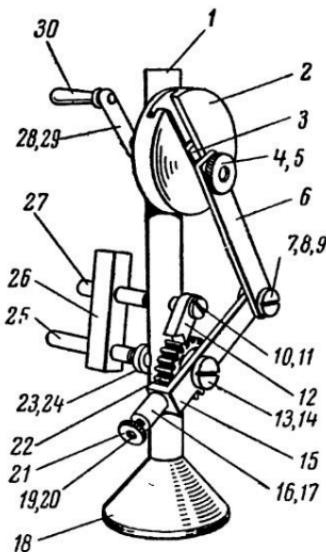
Модель механизма подачи стола поперечно-строгального станка: 1 — стойка; 2 — диск регулирования величины подачи; 3 — установочный палец; 4 — упорная втулка; 5 — гайка с накаткой; 6 — тяга; 7 — ось; 8 — шайба; 9 — гайка; 10 — винт крепления собачки храпового механизма; 11 — шайба; 12 — собачка храпового механизма; 13 — винт крепления коромысла; 14 — шайба; 15 — коромысло; 16 — гильза толкателя; 17 — нажимная пружина; 18 — основание; 19 — толкатель; 20 — шпилька крепления толкателя; 21 — головка толкателя; 22 — зубчатое колесо храпового механизма; 23 — стопорное кольцо; 24 — стопорный винт; 25 — «ходовой винт»; 26 — «стол»; 27 — направляющая «стола»; 28 — вал привода; 29 — рычаг привода; 30 — ручка.
